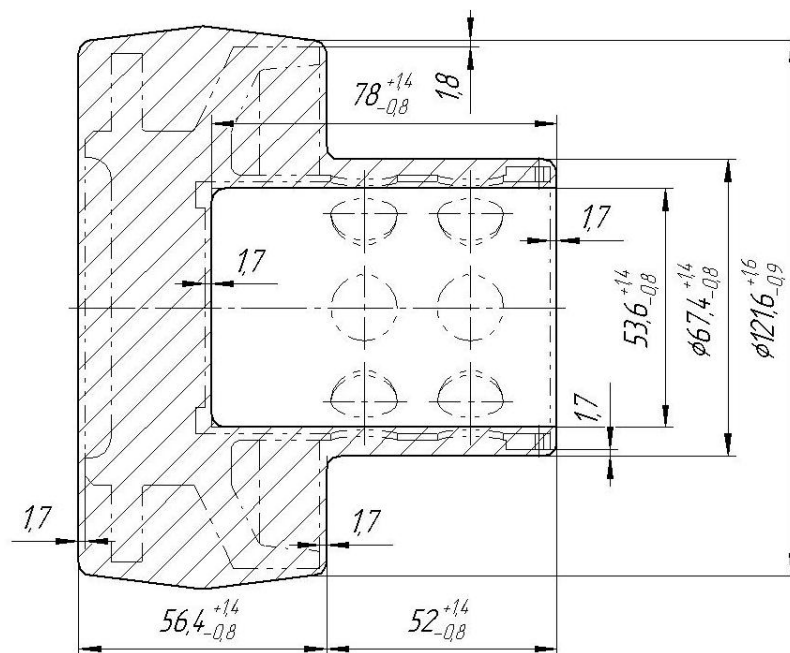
Эскиз заготовки – поковки-штампованной детали «Клапан»
